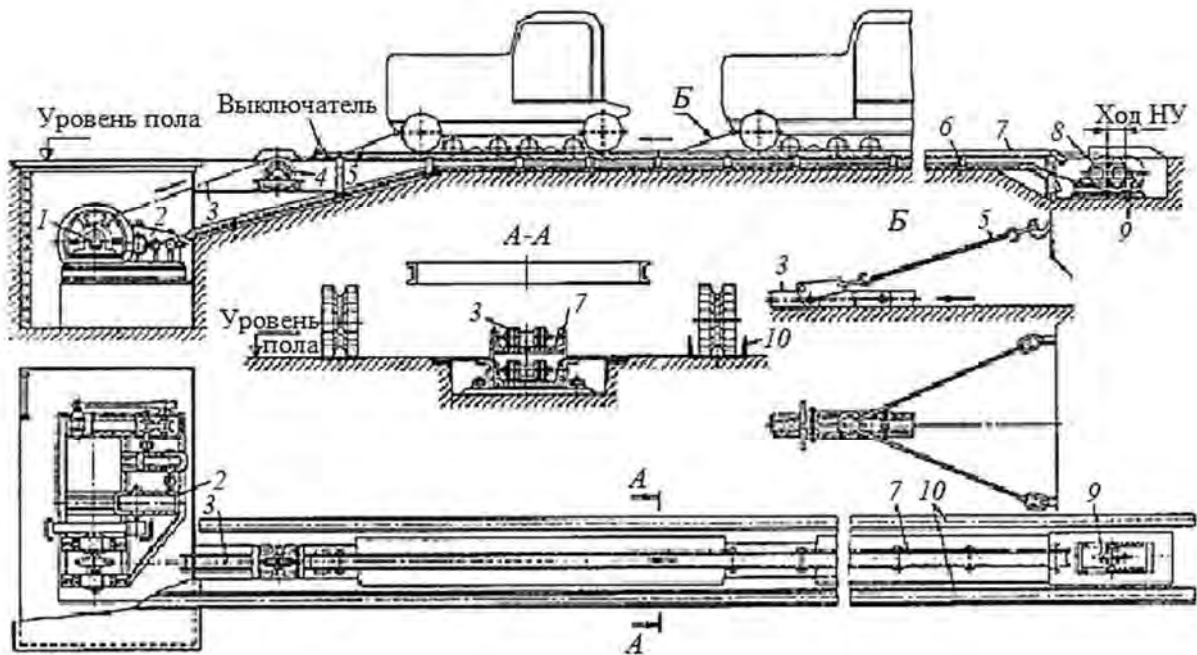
Вертикально замкнутый безтележечный грузоведущий конвейер с захватом за цепь конвейера для сборочной линии: 1 – приводная звездочка; 2 – привод; 3 – тяговая цепь; 4 – поворотное устройство; 5 – тяги; 6 – опорная металлоконструкция; 7 – направляющие пути; 8 – натяжная звездочка; 9 – натяжное устройство; 10 – специальные напольные пути
